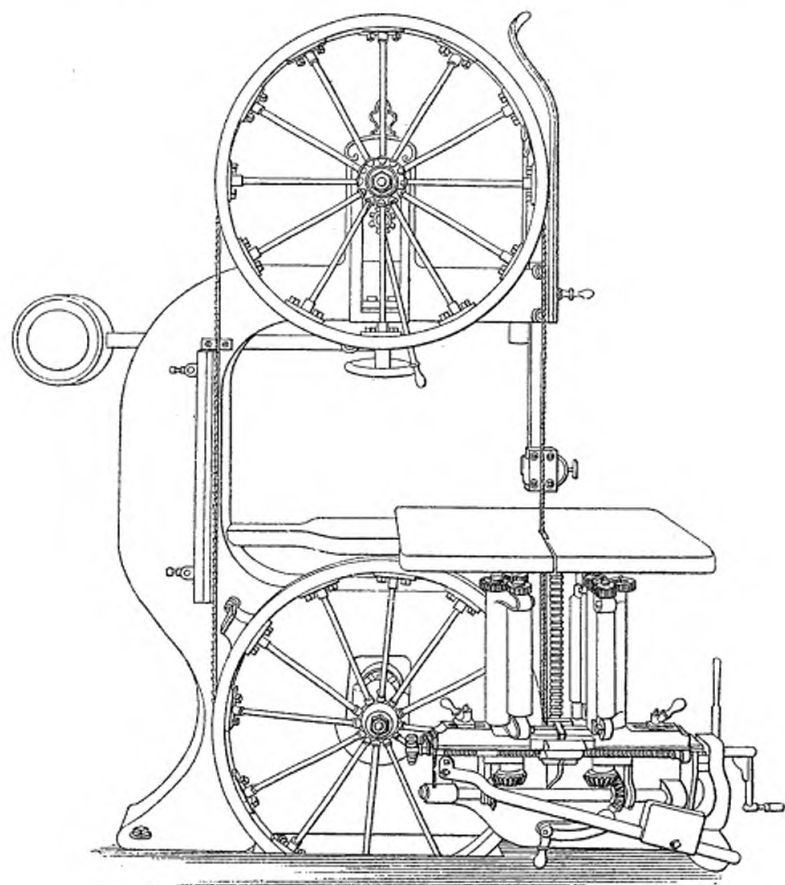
Machine à scier à refendre (le chariot étant descendu).
